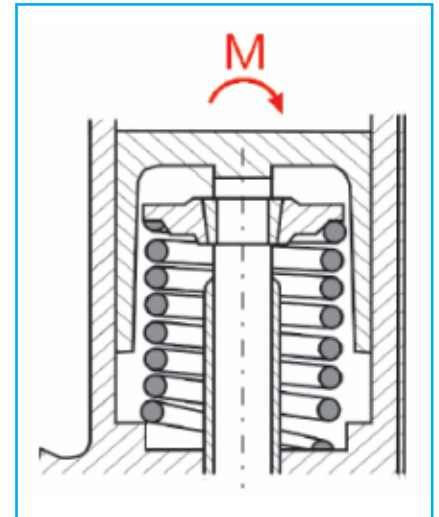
Resorte de válvula ladeado en el canto de fundición alzado
